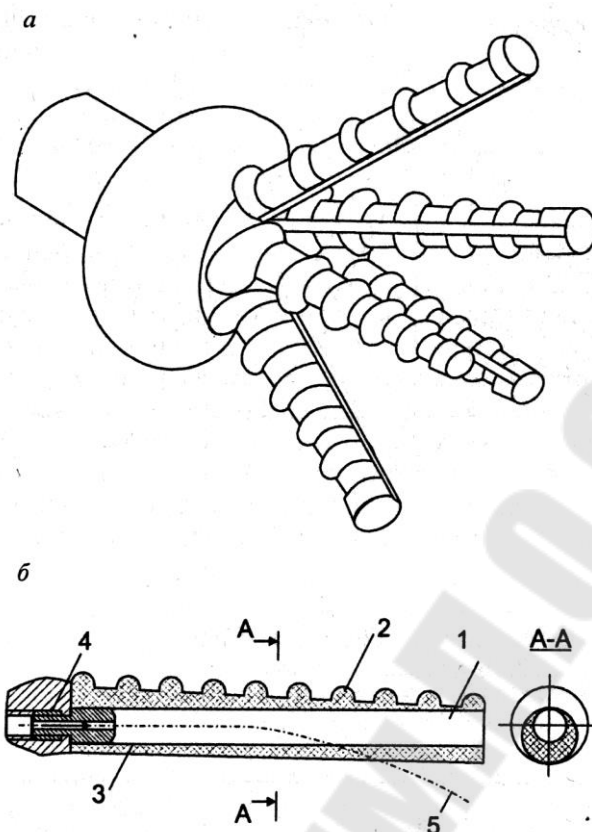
Пневматический схват с 5 гибкими надувными пальцами:
